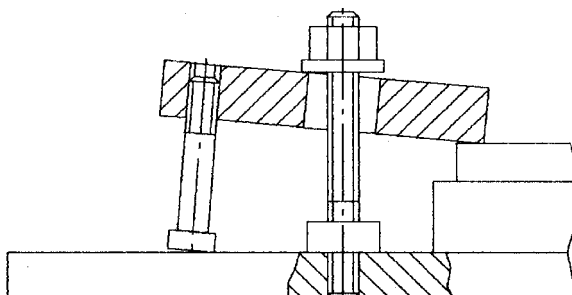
Конструкции винтов с различной опорной поверхностью
